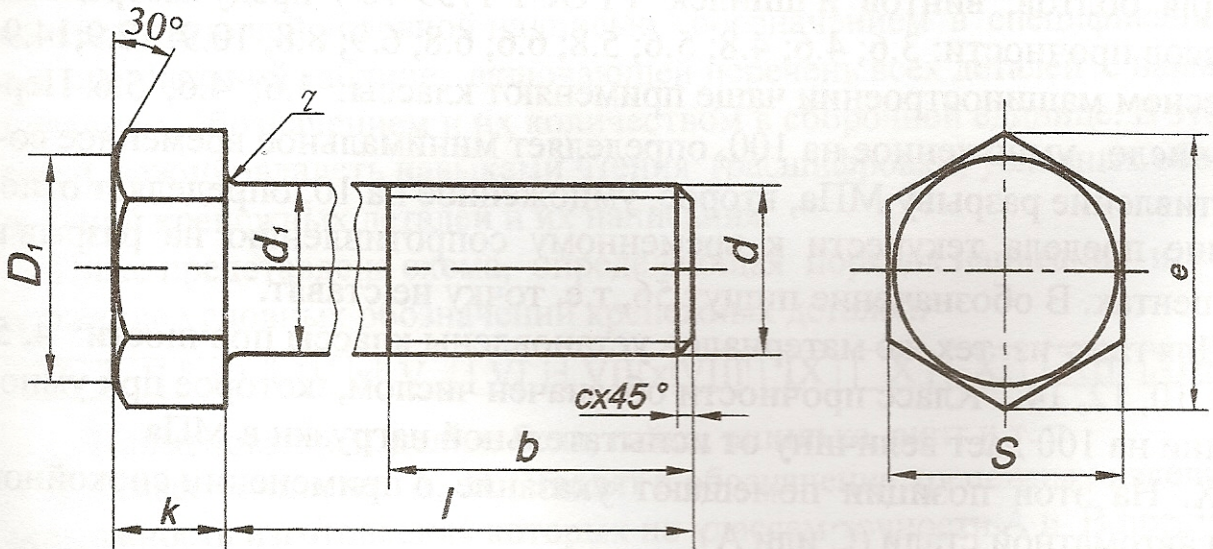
Чертеж болта: k - высота головки болта; d - диаметр резьбы; b - длина резьбы; l - длина болта; d_1 - диаметр стержня; r - радиус галтели; D_1 - диаметр основания фаски; ($D_1 = 0.9 - 0.95S$); e - диаметр описанной окружности; S - размер под ключ; s - высота фаски
